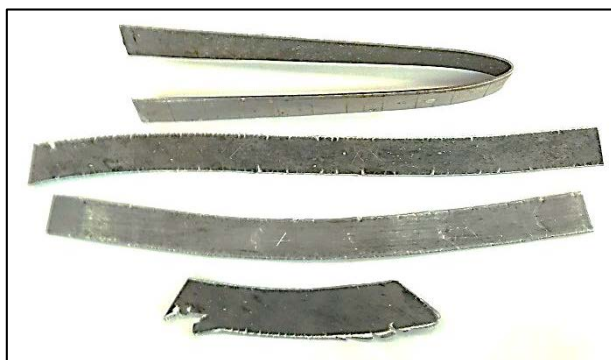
Биметаллические переходники «Al-сталь», полученные сваркой взрывом
